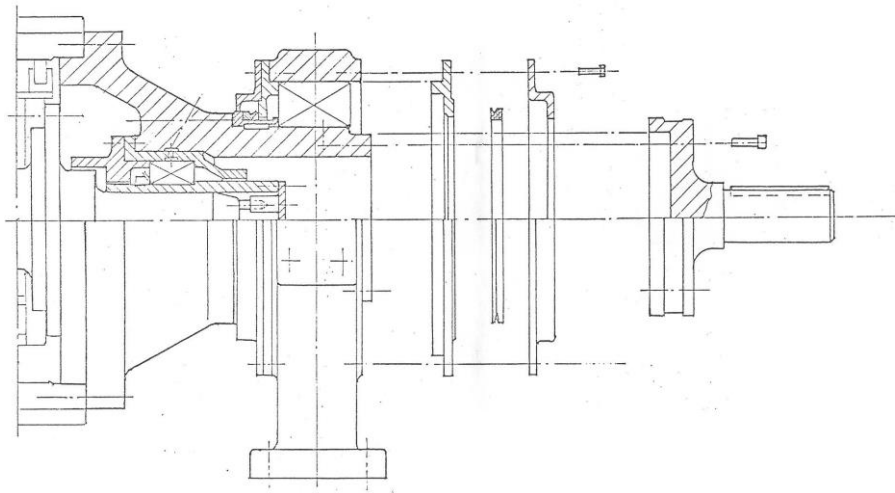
Конструкция подшипникового узла приводной стороны отсасывающего вала БДМ.
